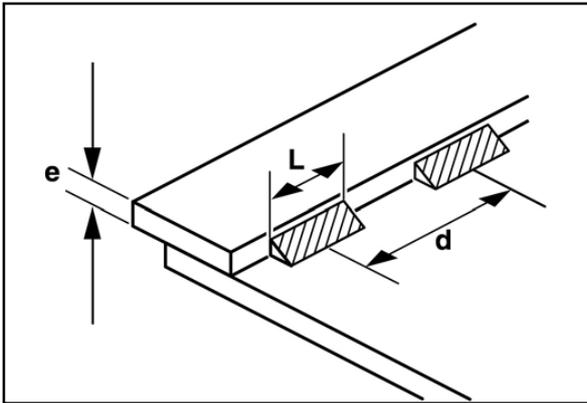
Соотношение толщины листа и расстояния между точками сварки
